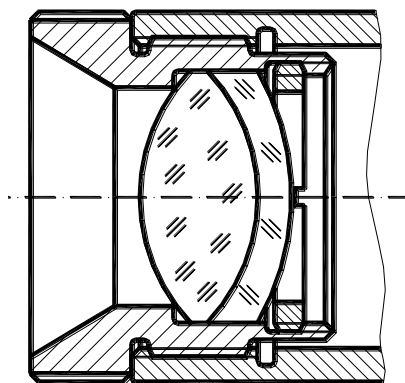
Soluție tradițională de fixare a componentelor optice prin îmbinare filetată
